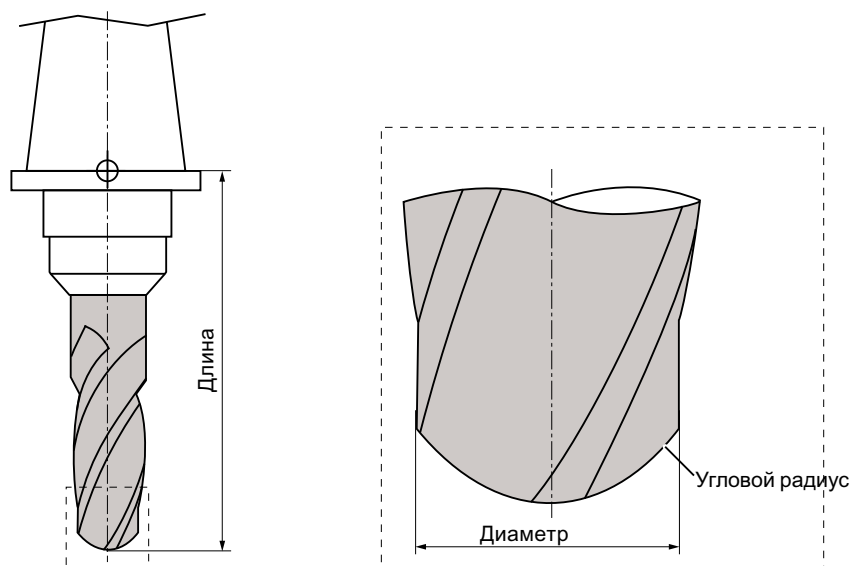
Тип инструмента 3D на примере сферической фрезы (тип 111)
